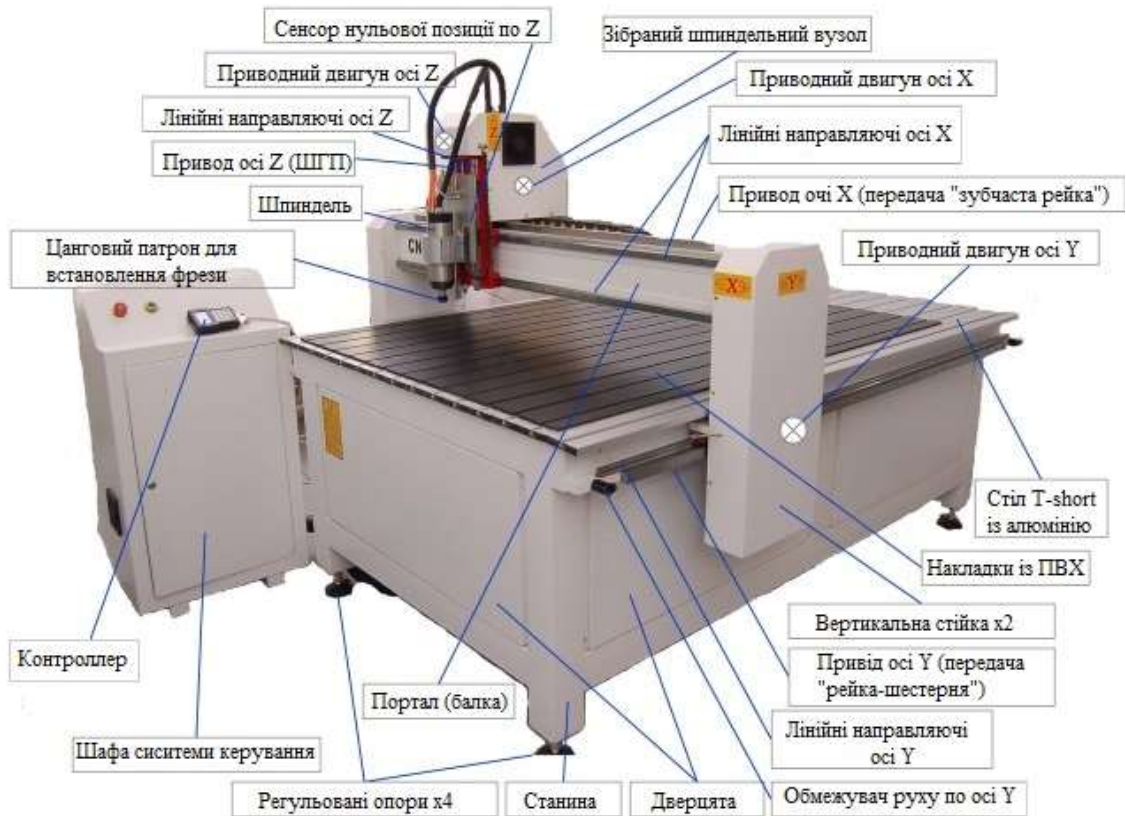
Зовнішній вигляд і будова портального фрезерного ЧПУ
